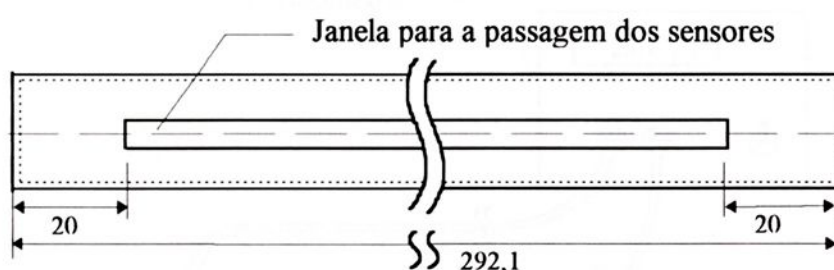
Esboço do cano de ferro com cotas em mm
